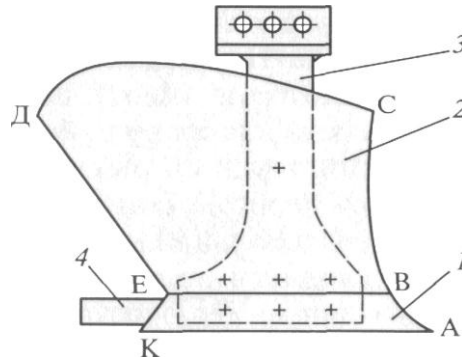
Корпус: 1 — леміш; 2 — відвальна частина; 3 — стійка; 4 — нижня частина.
